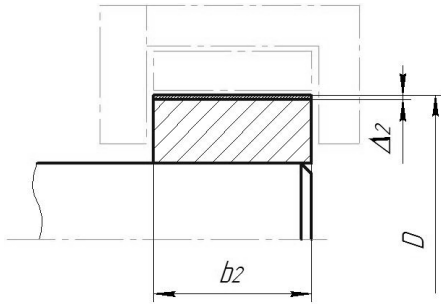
Схема нагрева детали в индукторе для разборки соединения
